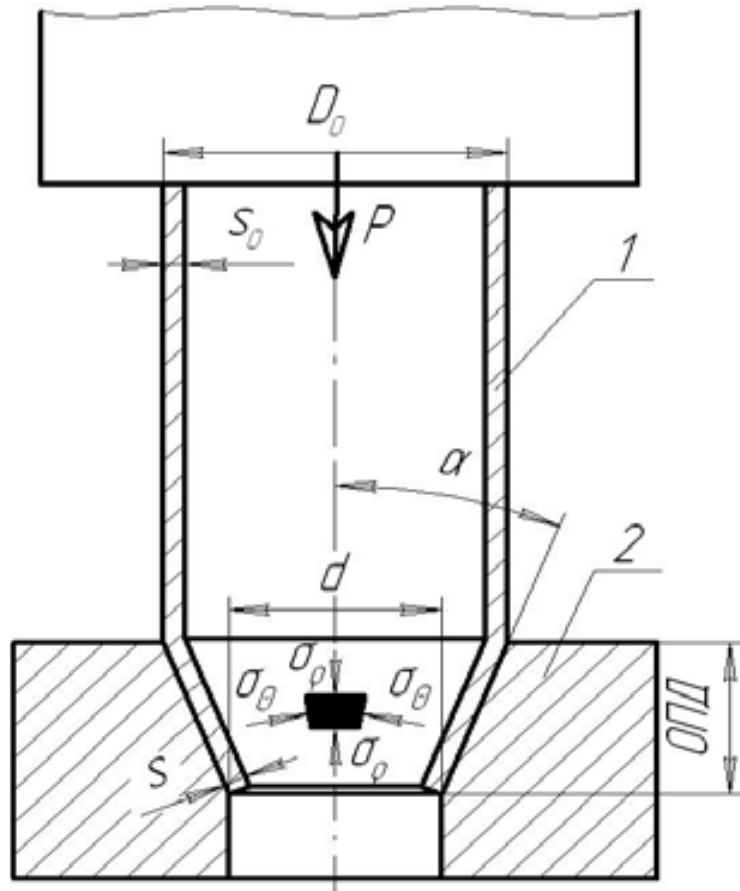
Технологічна схема обтиску трубної заготовки (1) в конічній матриці (2)
